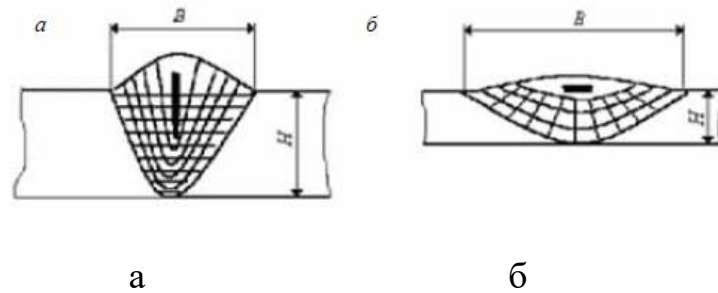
Вплив форми шва на хімічну неоднорідність (ліквацію) металу: а – вузький шов; б – широкий шов
